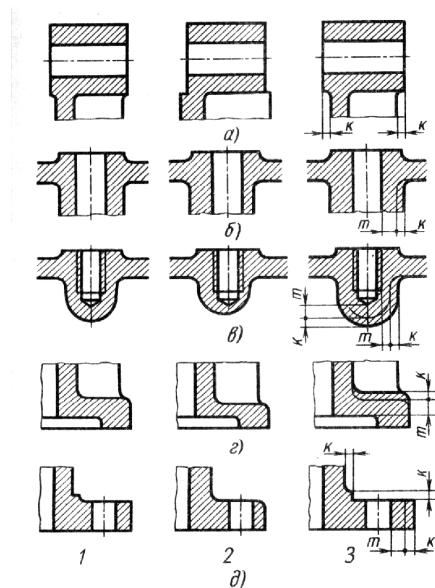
Сопряжения черновых и обработанных поверхностей контура стыка.
